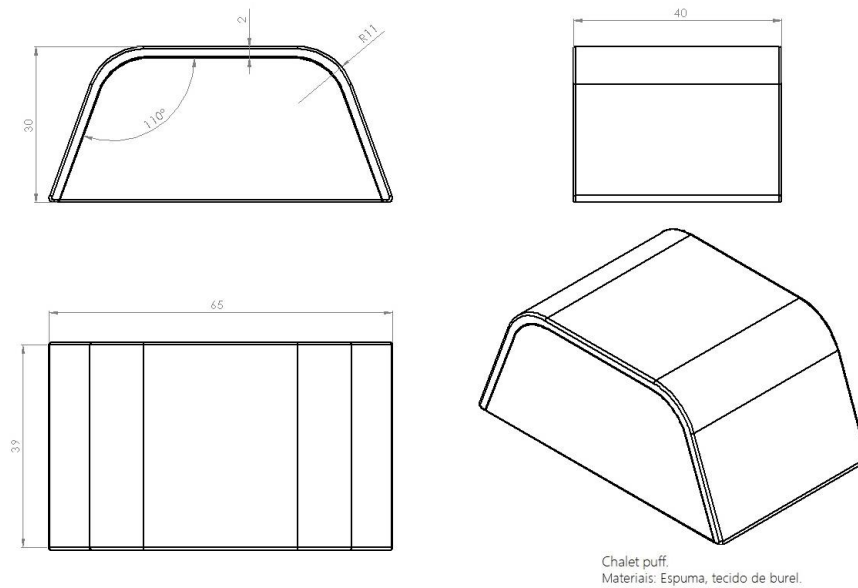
Desenho técnico CAD 3D do conceito *Chalet* (Fonte: Autor)
